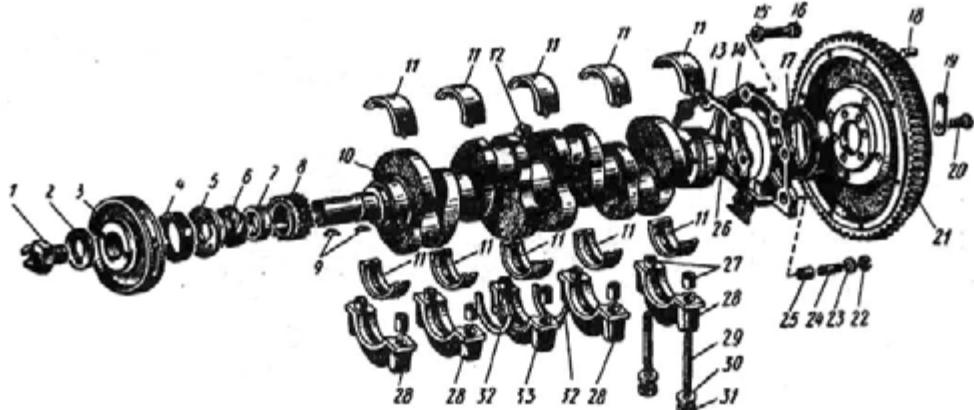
Коленчатый вал, складанный корсными подшипниками и маховик
